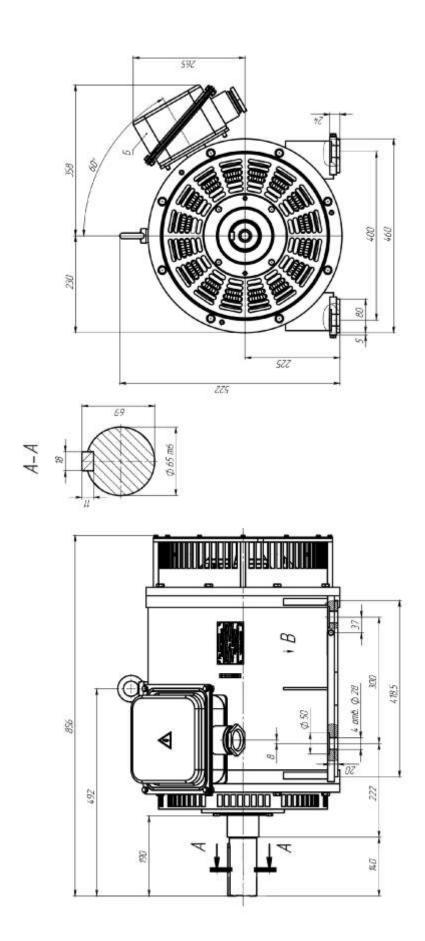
Габаритные, установочные и присоединительные размеры электродвигателя 4AЧ225S4. Масса двигателя (400 ± 20) кг
